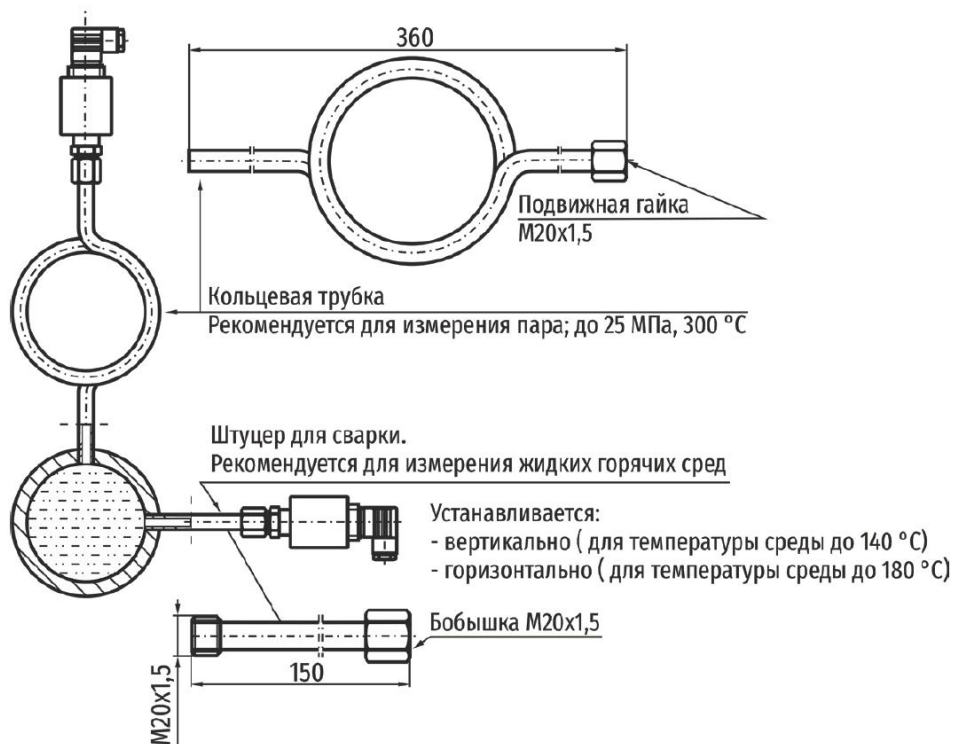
Примеры использования трубки кольцевой и штуцера для сварки с преобразователем давления APC-2000 для измерения горячих сред
